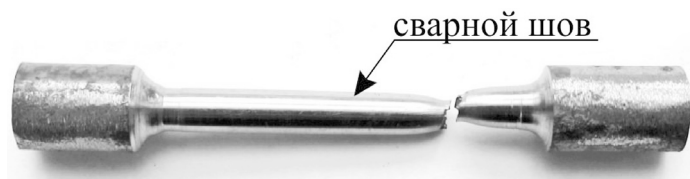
Сварной образец из титанового сплава, изготовленный по типу XIV, после испытаний на статическое растяжение
